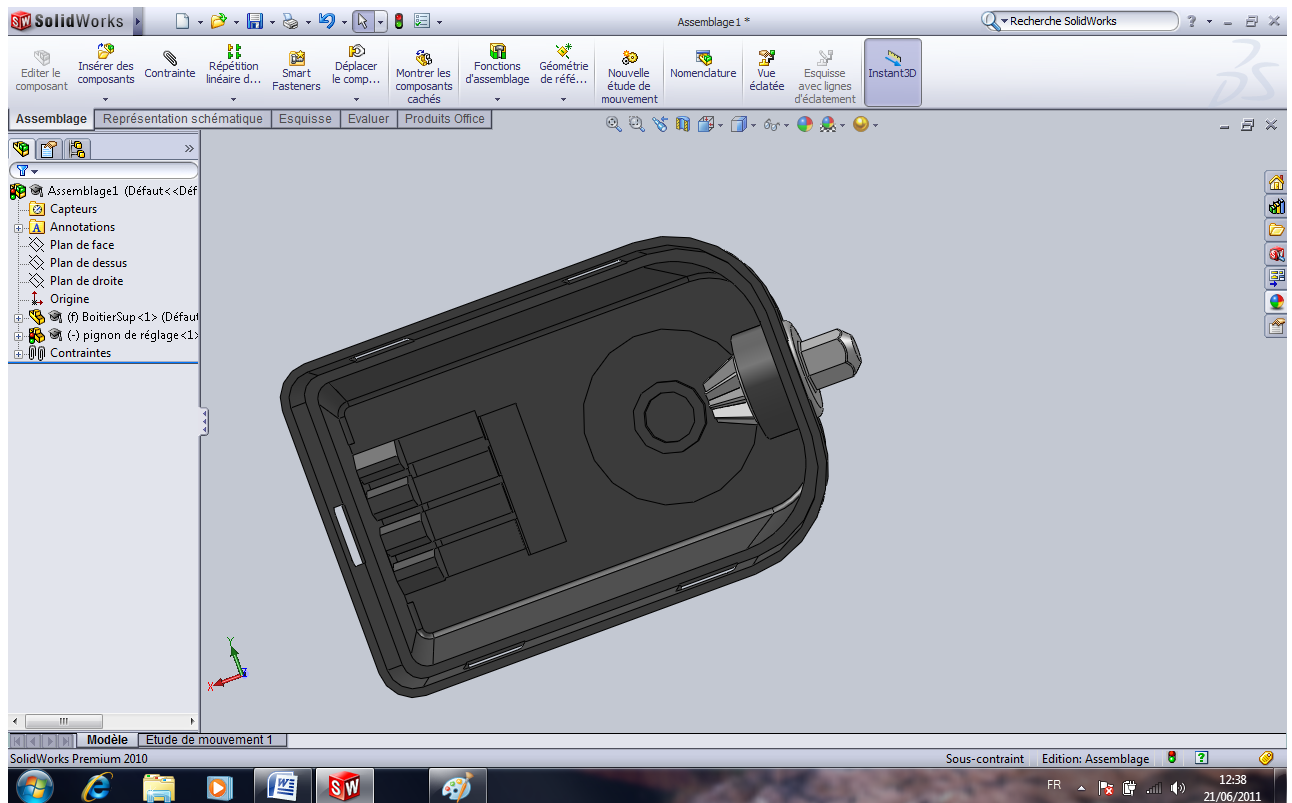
Assemblage 1 (boitier supérieur + pignon de réglage)
